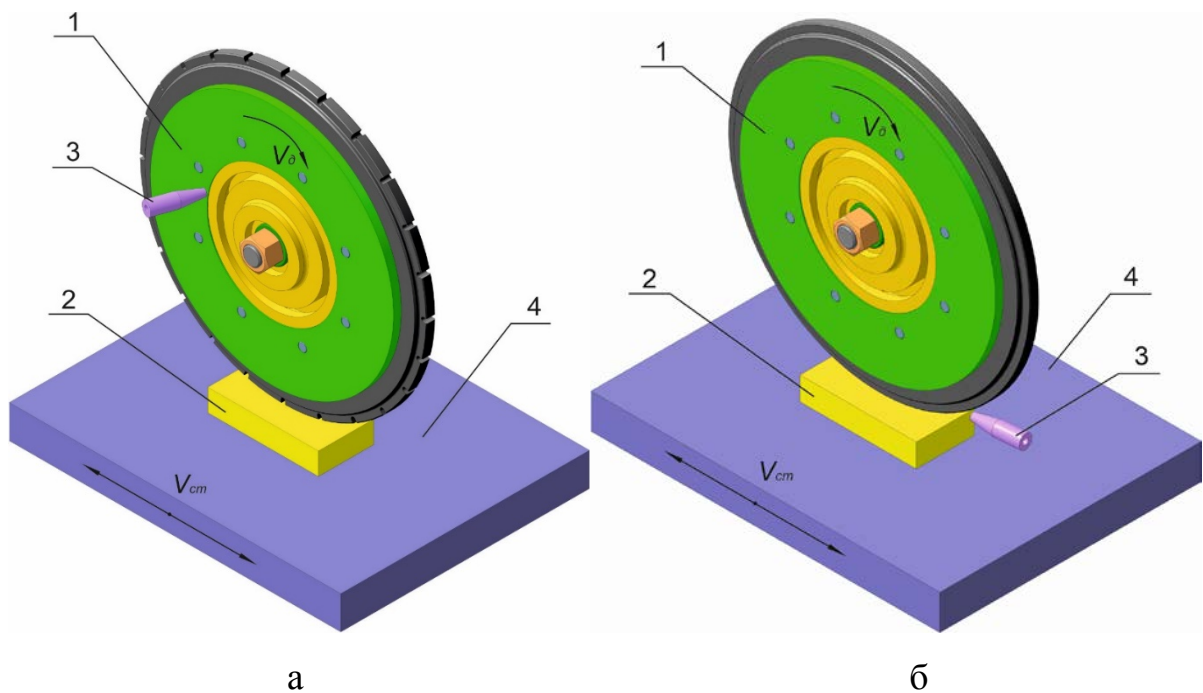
Схема фрикційної обробки плоских поверхонь деталей машин: а – подача середовища через канали, які виходять у паз інструмента, б – методом поливу. 1 – інструмент, 2 – оброблювальна плоска поверхня деталі, 3 – сопло для подачі технологічного середовища, 4 – стіл верстата
